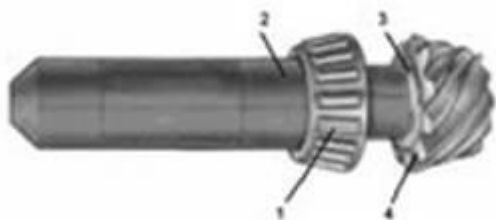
Установка внутреннего кольца заднего подшипника на ведущую шестерню: 1 — внутреннее кольцо заднего роликоподшипника; 2
